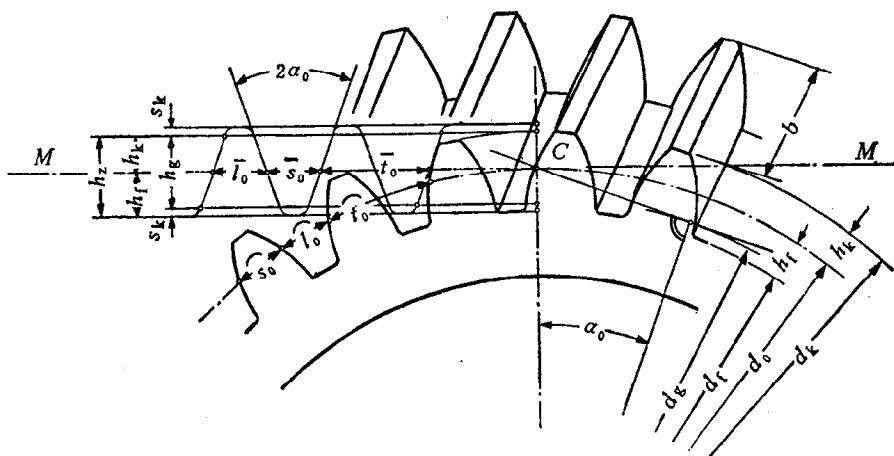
原始齿廓符合 DIN867 规定的直齿圆柱齿轮 MM 为
